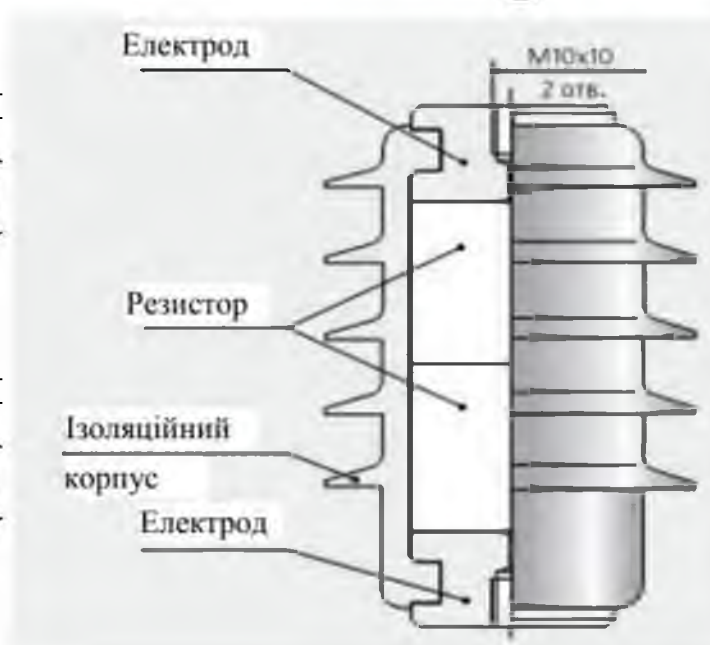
Поперечний розріз обмежувача перенапруг у порцеляновому корпусі
